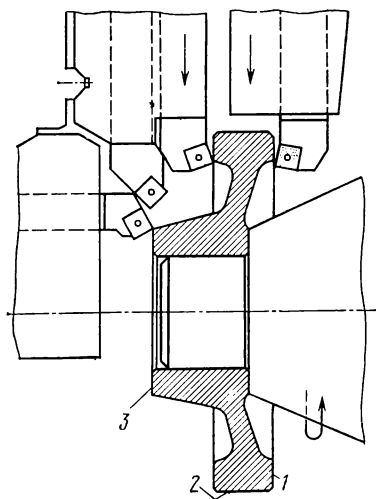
Схема обработки базовых поверхностей заготовки колеса-диска
